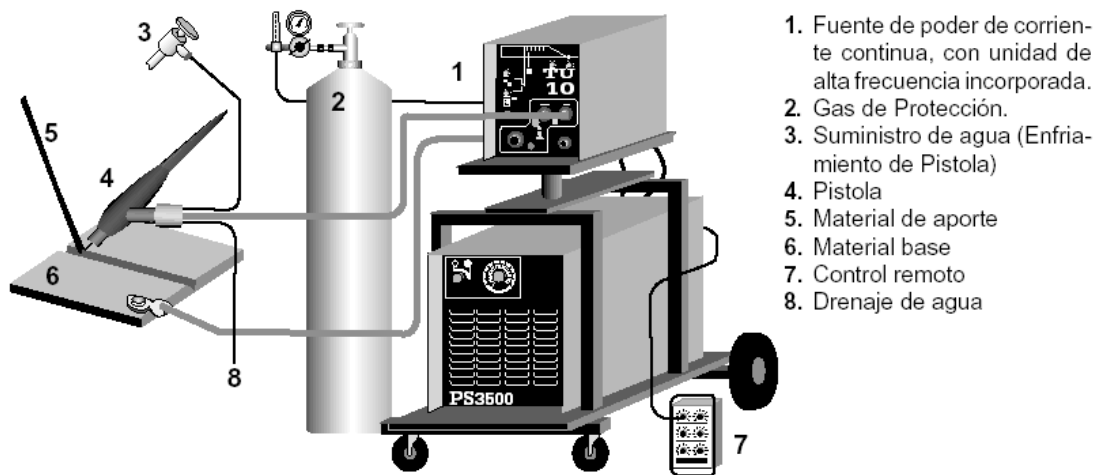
Conexiones principales de una instalación de última generación para la soldadura GTAW.
